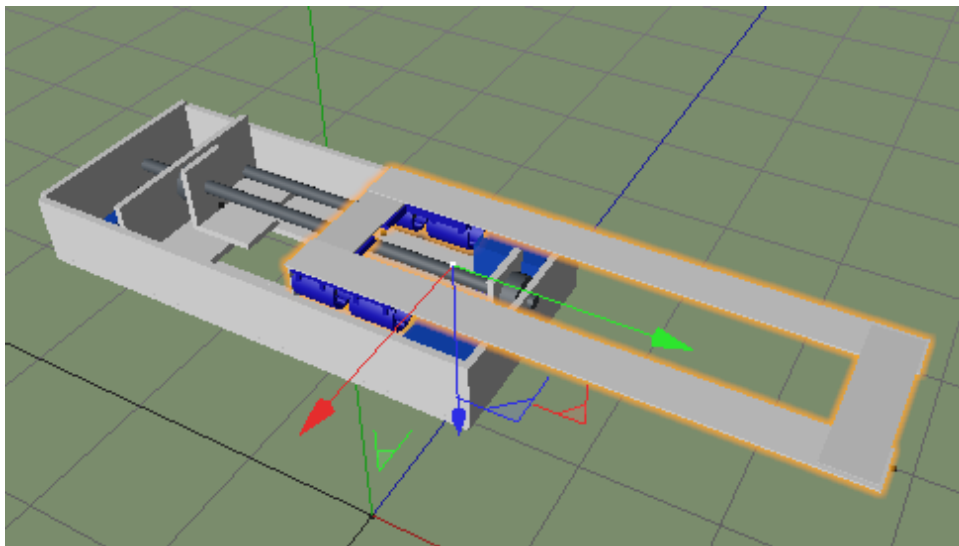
b) Sistema de deslizamiento con plancha deslizado.
